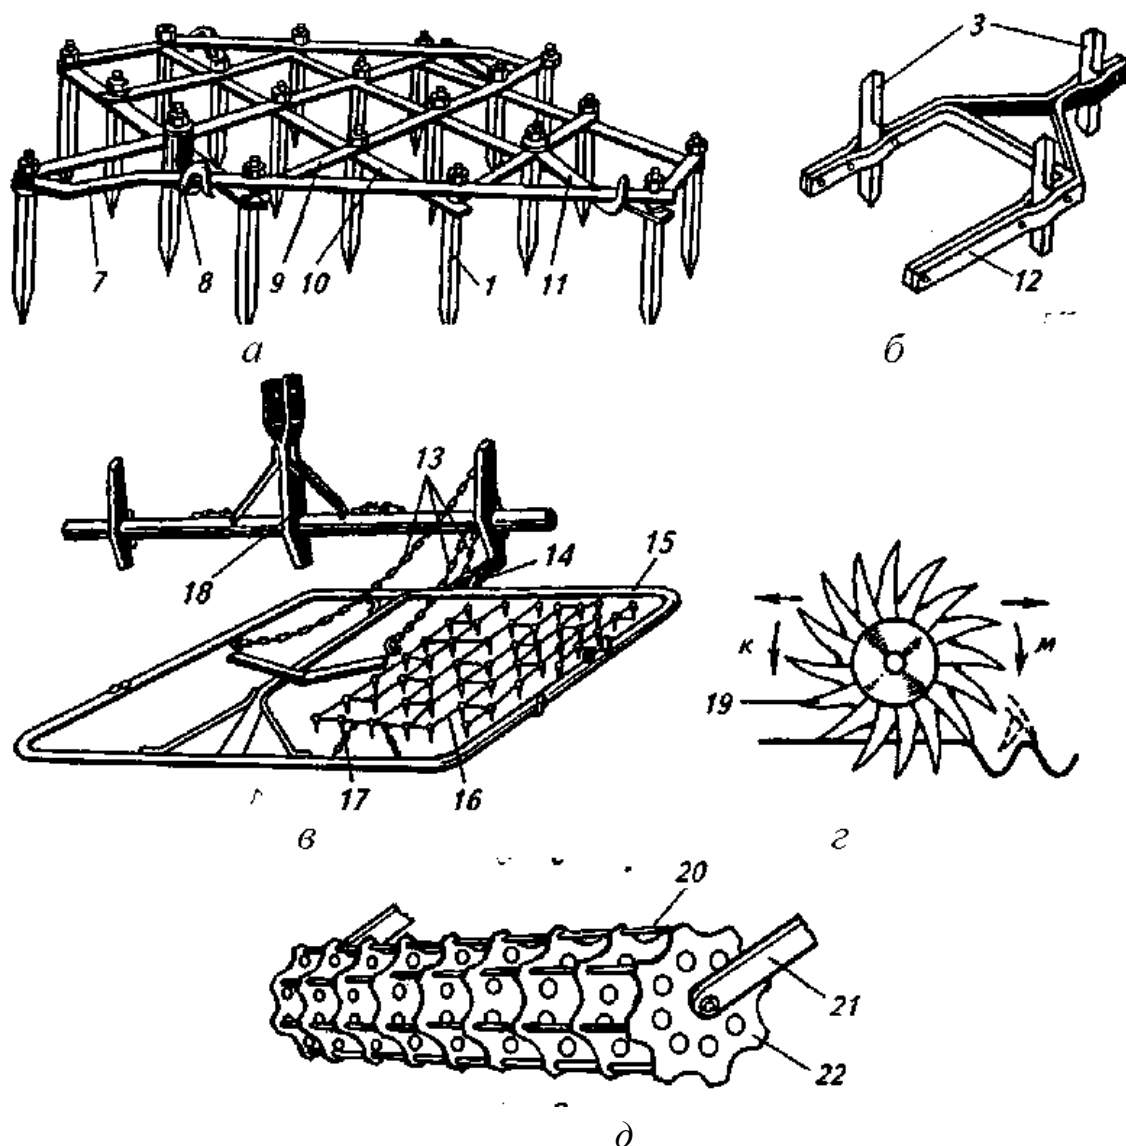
Бороны: а – общий вид бороны БЗТС-1; б – звено луговой бороны; в – общий вид сетчатой бороны БСО-4; г – игольчатый диск мотыги; д – секция прутковой бороны; 1 – зуб квадратного сечения; 3 – ножевидный зуб; 7, 9, 10 – планки; 8 – крюк; 11 – прицепное устройство; 12 – рамка звена; 13, 17 – цепи; 14 – тяга; 15 – рамка бороны; 16 – сетчатое полотно; 18 – навеска НУБ-4,8; 19 – вогнутые зубья; 20 – пруток; 21 – планка прицепа; 22 – диск
